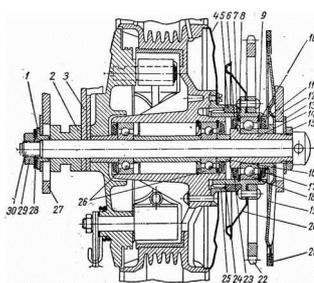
Разрез ступицы заднего колеса и звездочки:
